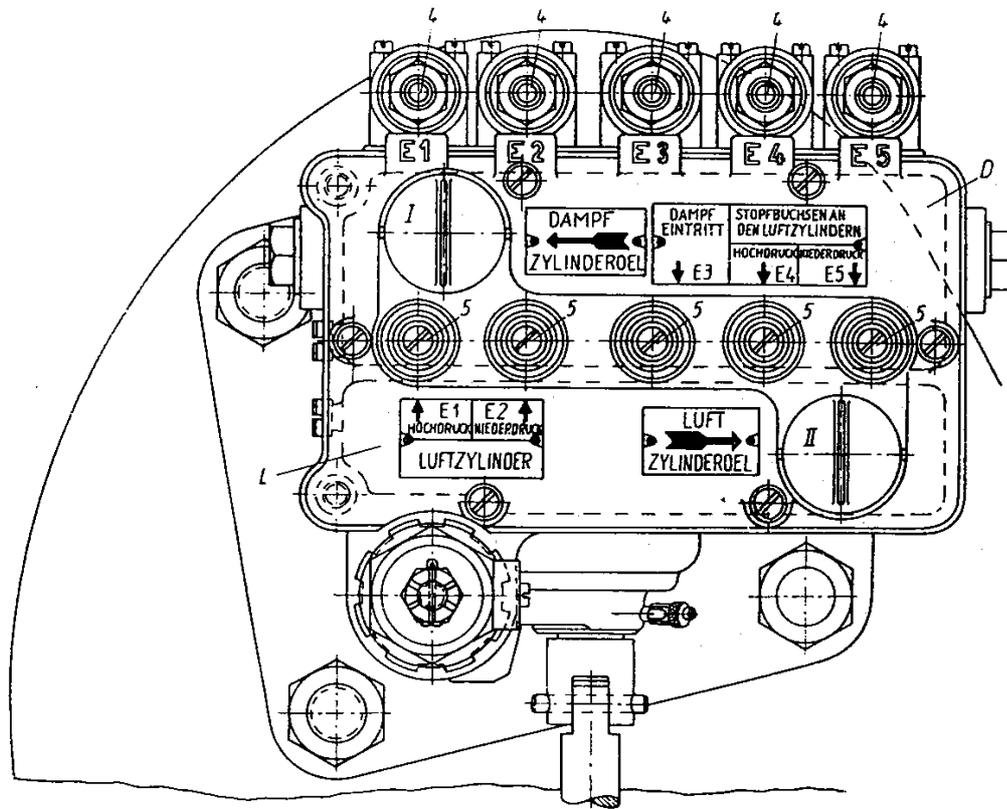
Aufsicht auf die Schmierpumpe mit 5 Schmierstellen
